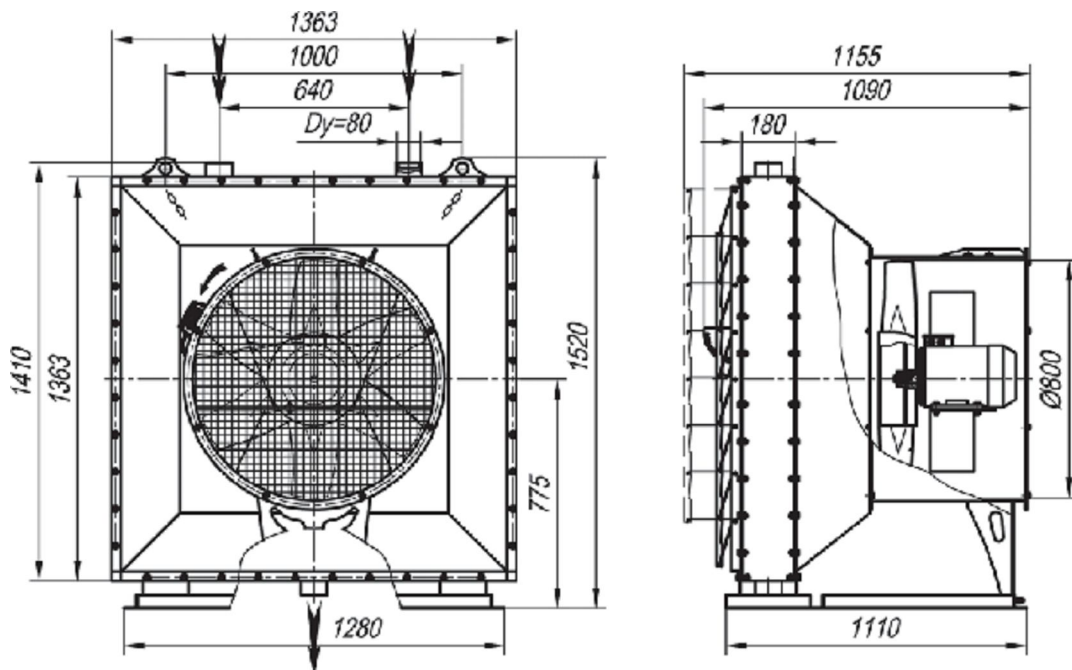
Габаритные и присоединительные размеры агрегата воздушно-отопительного СТД-300П на базе парового воздухонагревателя типа КП.
